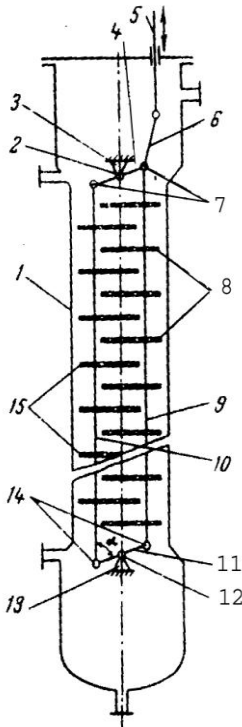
Колонный аппарат. 1 – корпус; 2,12 – опоры; 4,11 – коромысла; 5- шток; 6 – поводок; 7,14 – шарнир-коромысла; 8,15 – диски насадки; 9,10 – штанги
